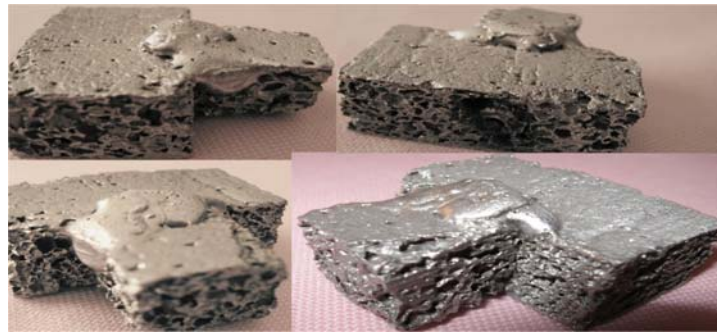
Provete soldado por MIG de diversas vistas.
